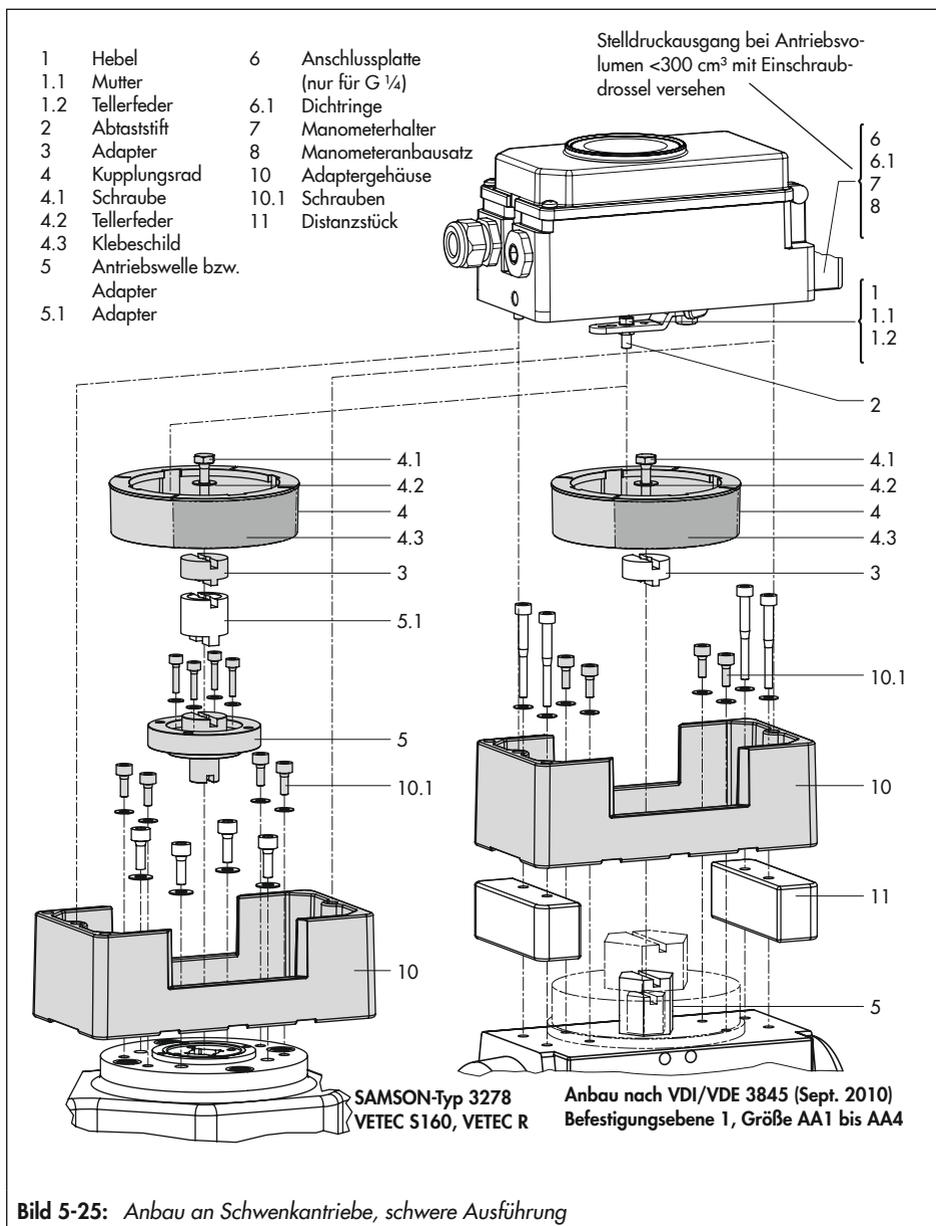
Anbau an Schwenkantriebe, schwere Ausführung
